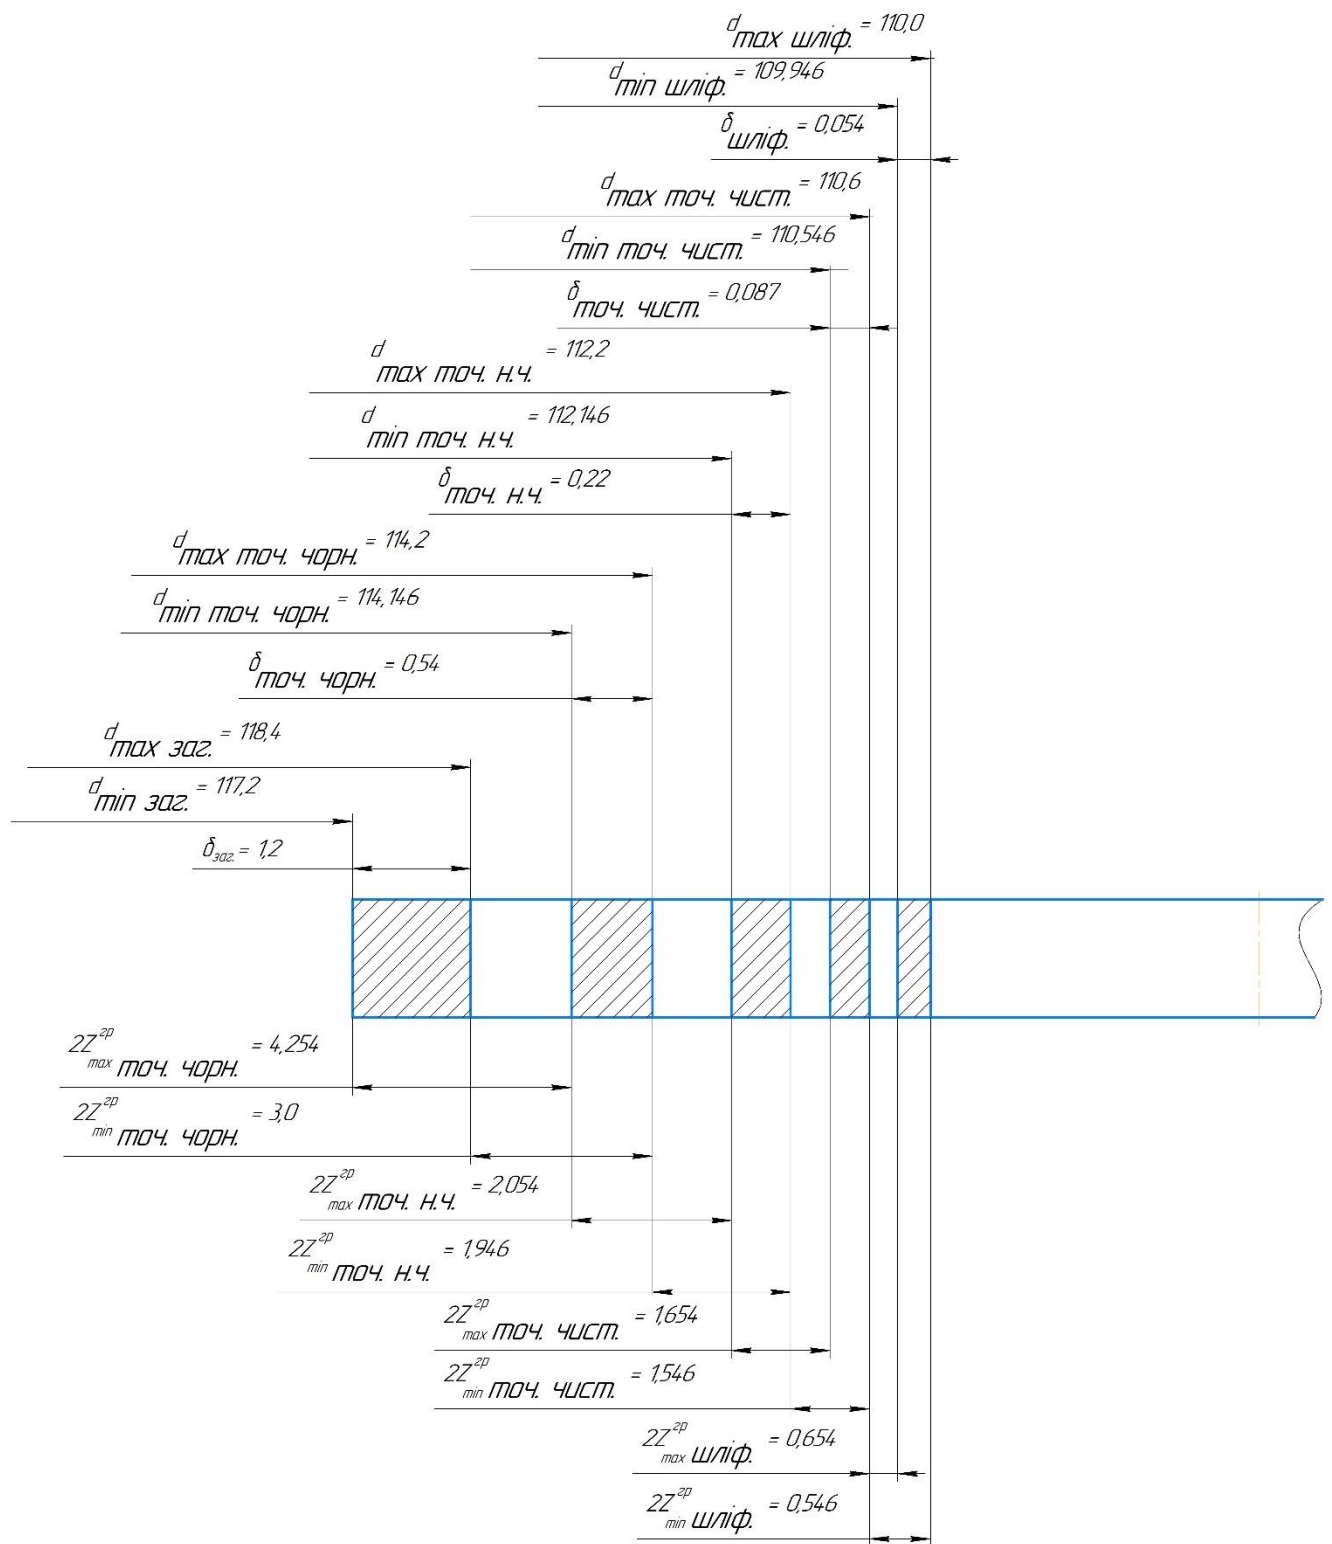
Схема графічного розташування припусків і допусків для зовнішньої циліндричної поверхні $\varnothing 110_{-0,054}$
